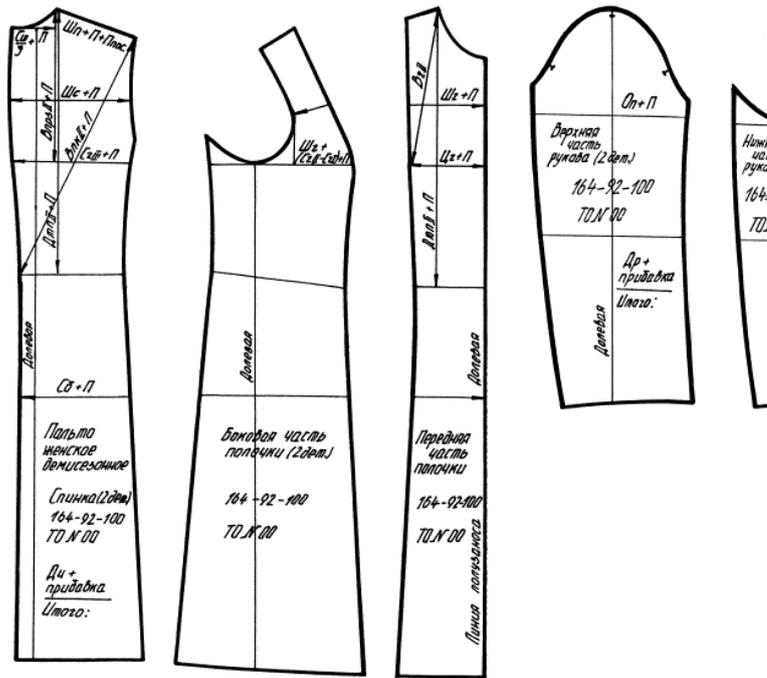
Рабочие чертежи лекал базовых конструкций
